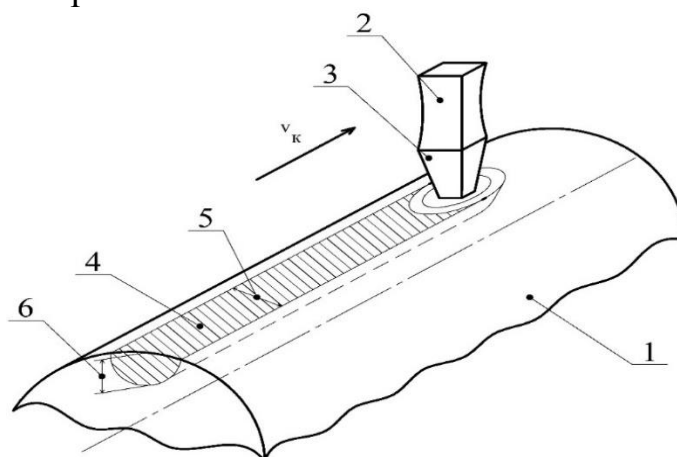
Схема предварительного локального криогенного воздействия на поверхность цилиндрической заготовки, где: 1 – цилиндрическая заготовка; 2 – устройство с жидким азотом; 3 – сопло устройства с жидким азотом; 4 – метастабильная структура; 5 – ширина метастабильной структуры; 6 – глубина метастабильной структуры
